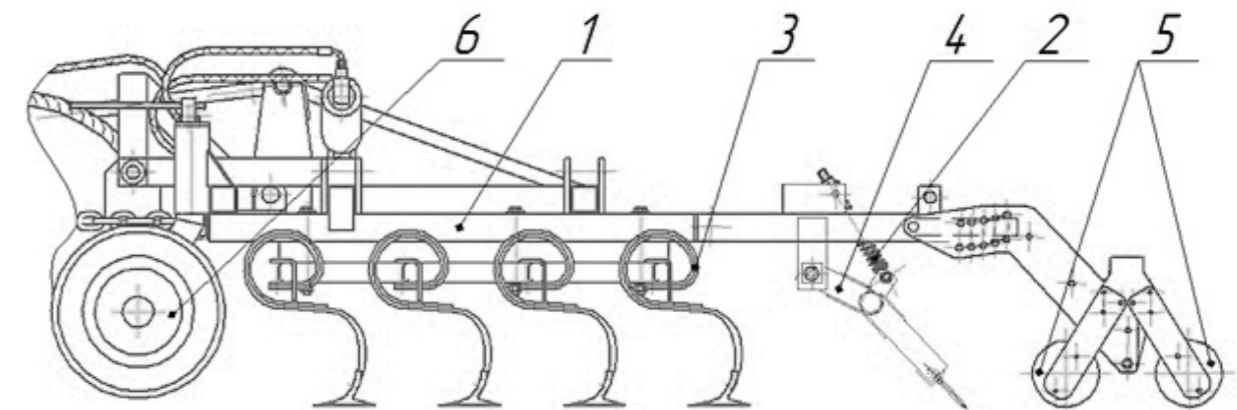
з *Культиватор прицепной КБМ-10,8ПС-4Д.
